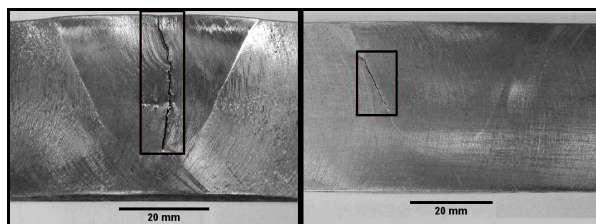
Perfil horizontal das soldas com carga de 100 kN com recalque.
